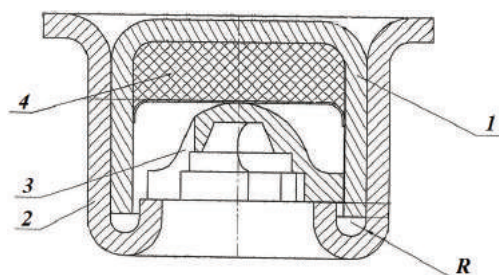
Конструкция нового капсюля-воспламенителя «КВ-Б»:
